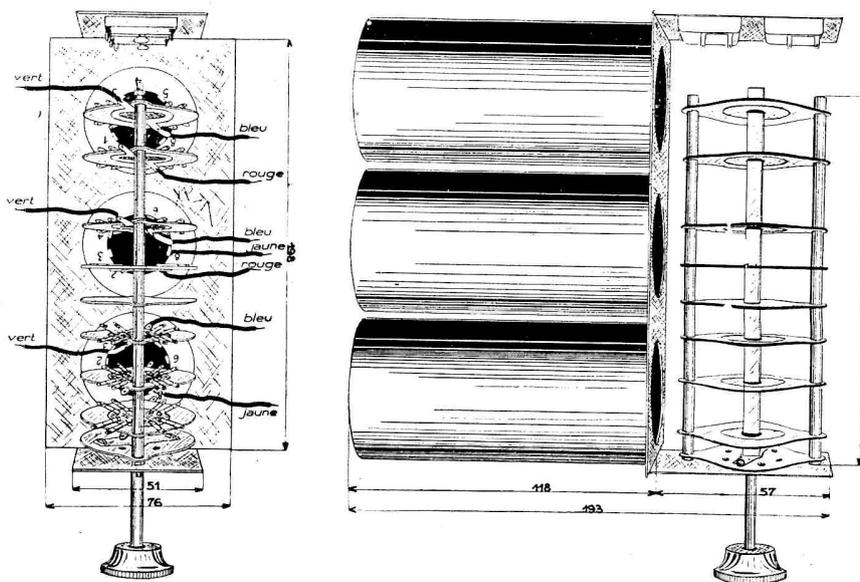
Vue par dessous et vue de côté du bloc de bobinages
